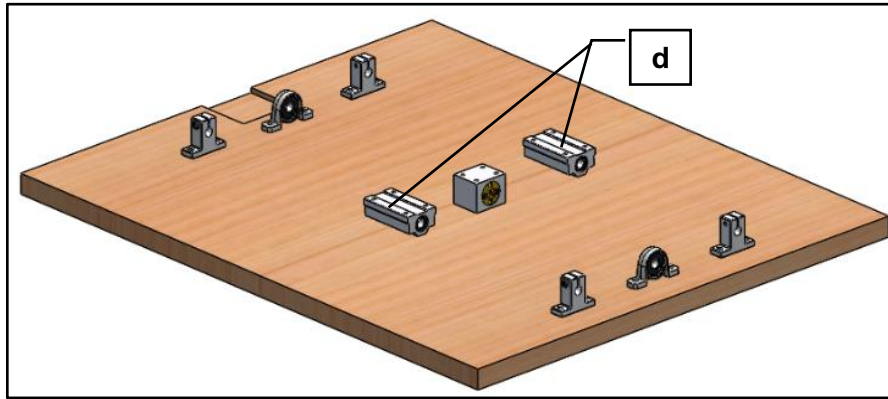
Perspectiva del posicionamiento del rodamiento lineal con soporte largo SC8LUU y el ensamblado del bloque de aluminio con la tuerca de bronce M8
